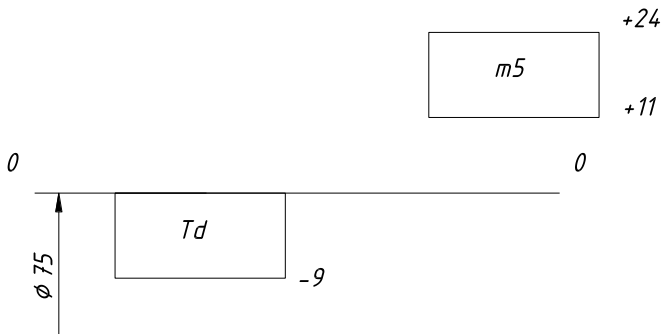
Схема розташування полів допусків валу і внутрішнього кільця підшипника
